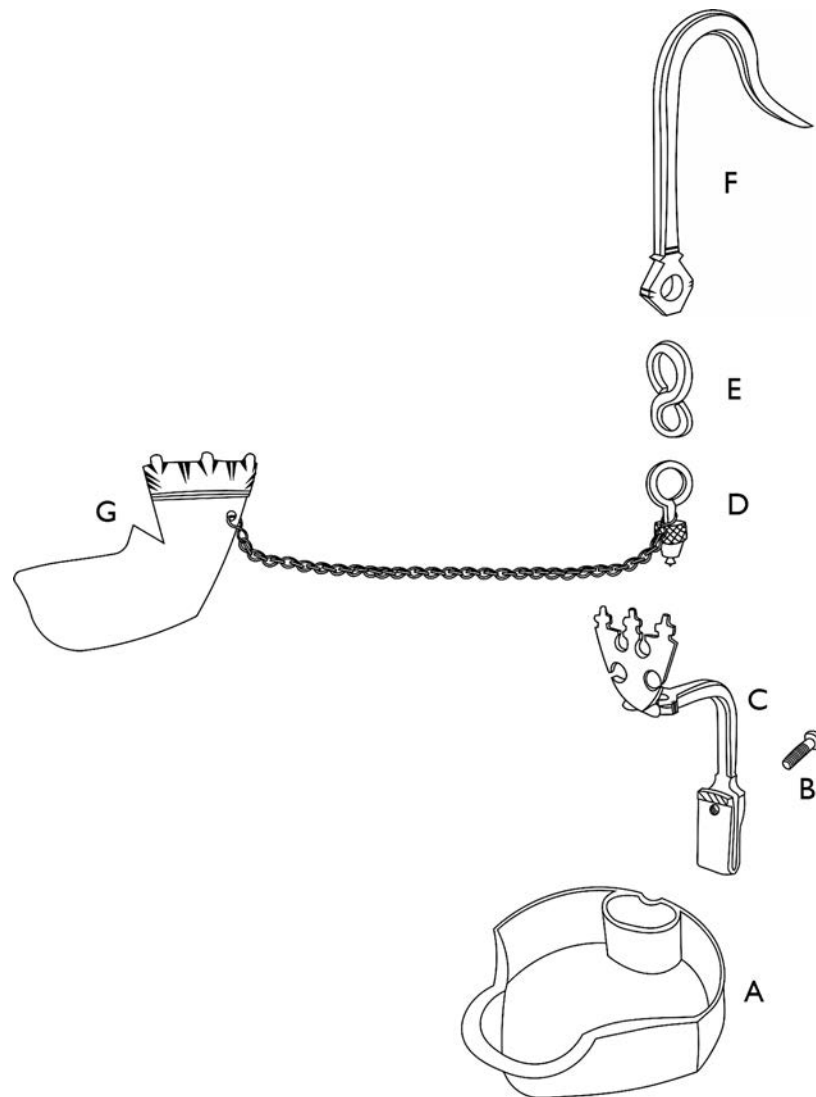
Explosionszeichnung einer eisernen sächsischen Unschlitt-Grubenlampe, Anfang bis Mitte 18. Jahrhundert. Diese Form mit Kreuzschild, in einer Bügeltülle verschraubtem Bügel, Wirbel mit stilisierter Eichel als Drehlager und metallinem Dochniederhalter (Dochtblech, »Leichtstein«, Schurblech, Schürblech) ist bereits als ausgebildete Spätform anzusprechen, die allerdings auch bereits im 17. Jahrhundert Vorbild für originäre Unschlittlampen aus der Montanregion Harz war (vgl. Büttner 2026, S. 321 ff.). Ersichtlich wird, dass die Form der Lampenschale auf die Grundform der spätmittelalterlichen Tonschalenlampen zurückgeht. Die Griff-tülle der Tonschalenlampe wird zur Tülle für das Einsetzen des überwölbenden Lampenbügels. A – Lampenschale; B – Bügel-schraube; C – Bügel mit Kreuzschild; D – Wirbel mit Eichel als Drehlager; E – Zwischenglied; F – Haken; G – Dochtblech. (Grafik: © Jan Büttner)
